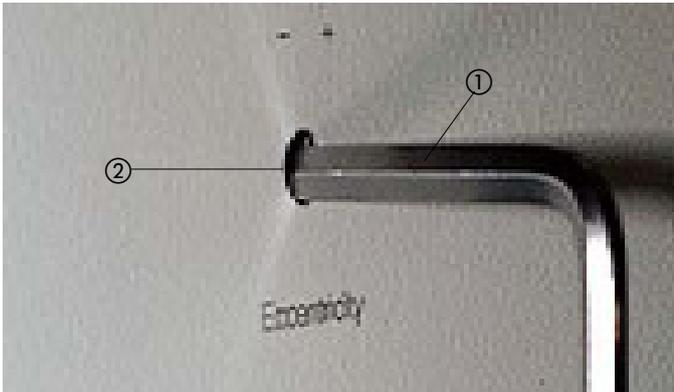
Einführen des Werkzeugs zur Einstellung der Auslenkung
